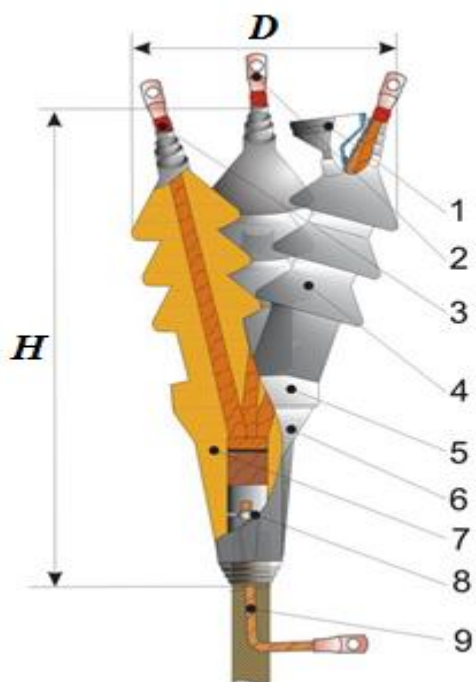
,в. Муфта эпоксидная концевая на напряжения 6 и 10 кВ: 1 – воронка для заливки эпоксидного компаунда; 2 – наконечник обеспечивающий электрический контакт жил; 3 – подмотка лентой ЛЭТСАР; 4 – изолятор; 5 – крышка; 6 – корпус муфты; 7 – компаунд, служащий для электрической изоляции и герметизации муфты; 8 – бандаж из проволоки закрепляющий провод заземления с наконечником; 9 – провод заземления с наконечником
